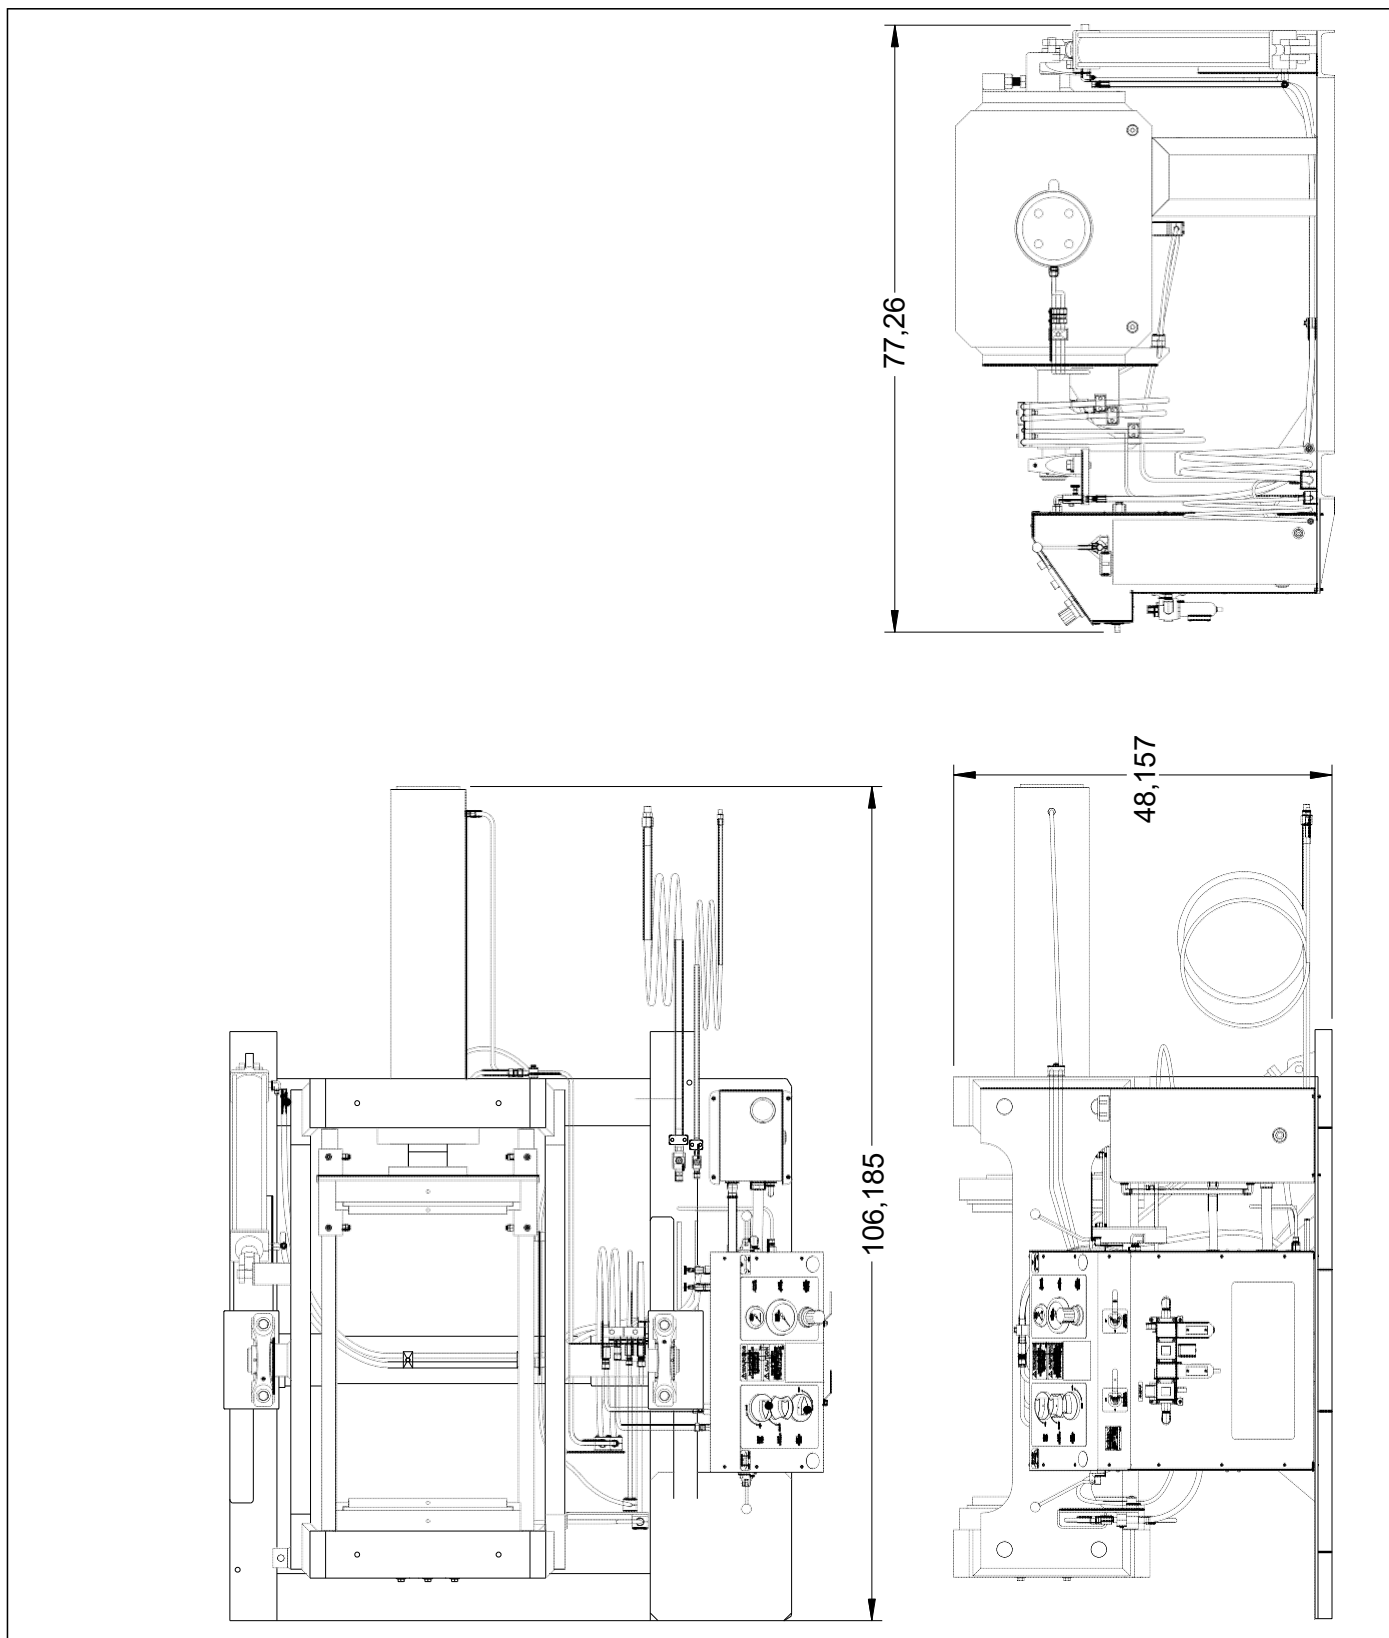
DIMENSIONES DE LA MORDAZA
